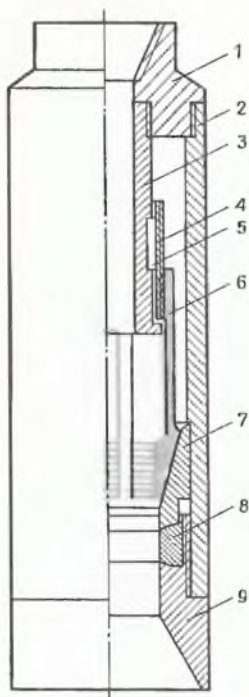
Труболовка наружная освобождающаяся (ТНП)
